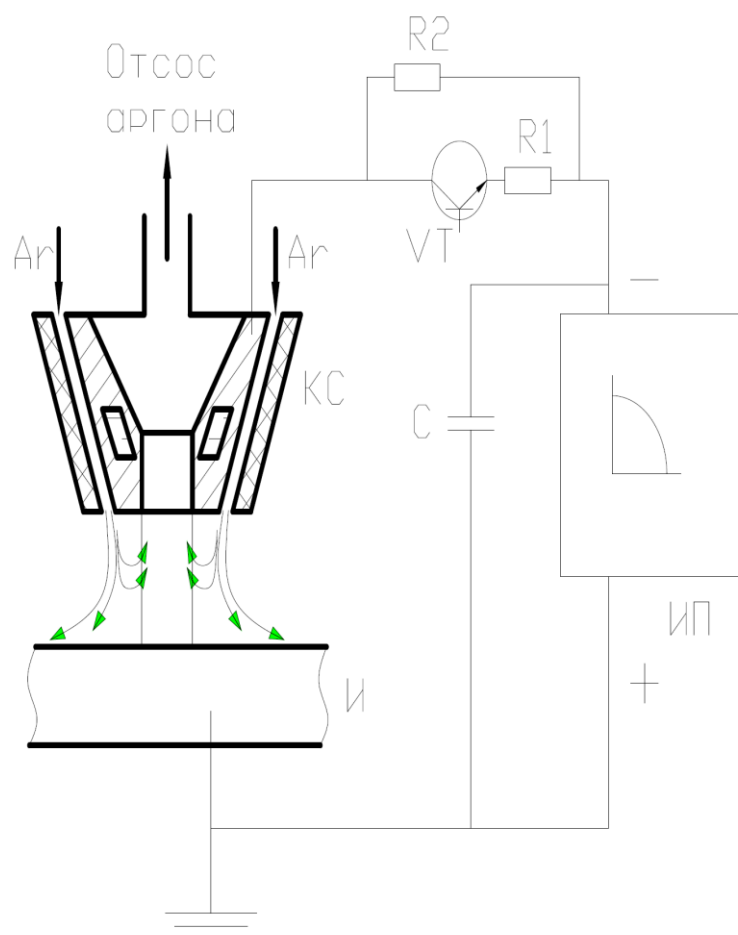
Схема сварки неплавящимся электродом
